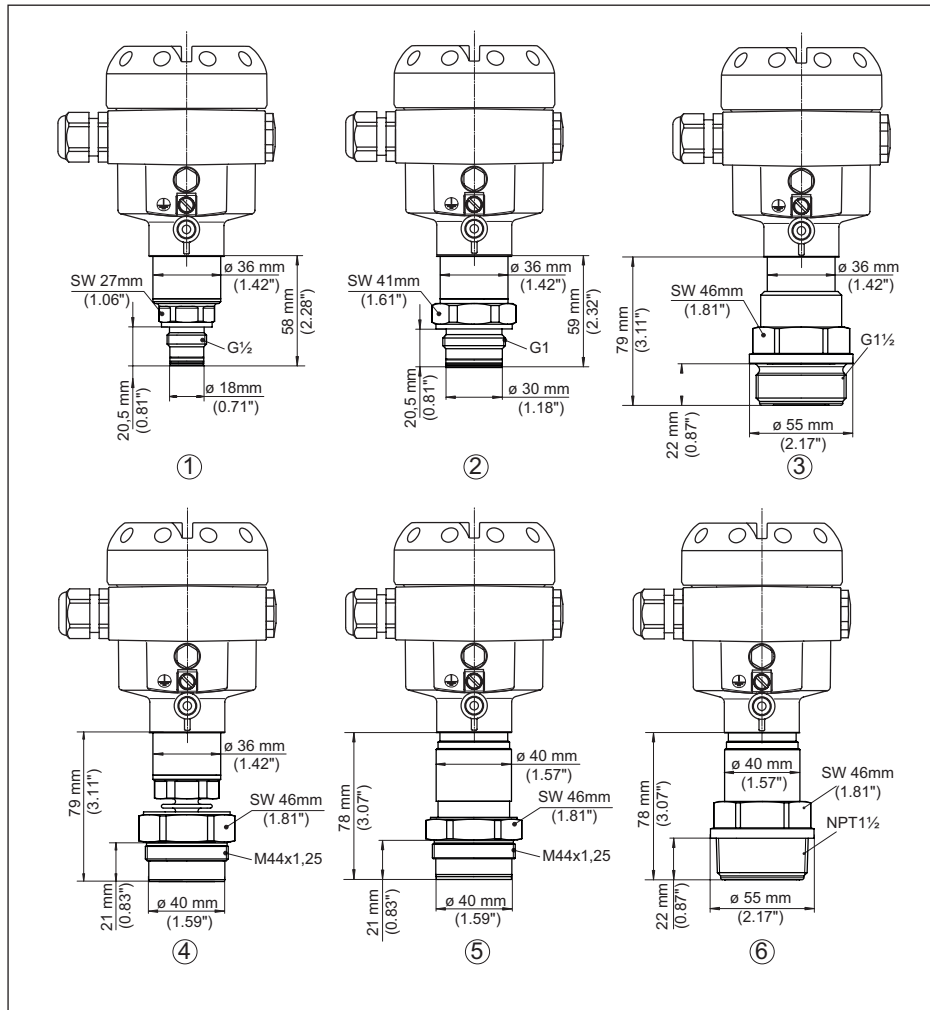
IPT-2x, Gewindeanschluss frontbündig
